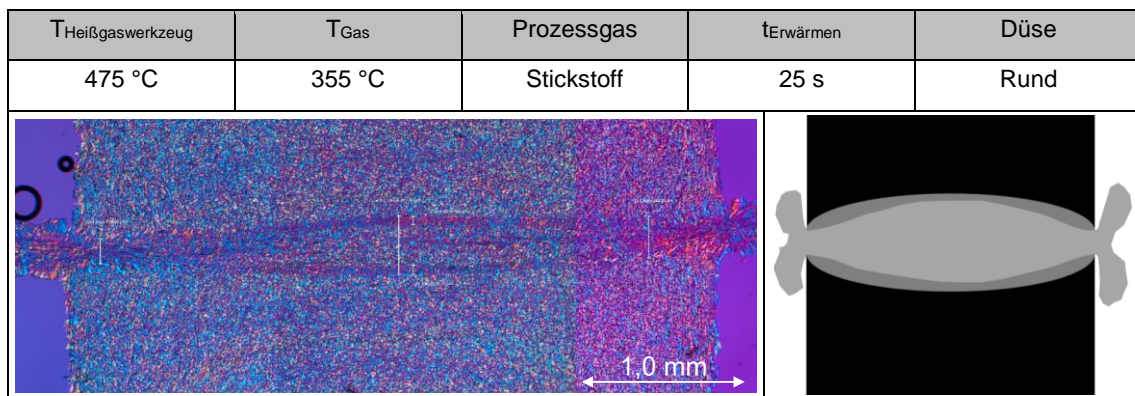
Dünnschnittaufnahme einer mit Rund-Düse erwärmten Schweißnaht mit elliptisch aufgeschmolzenem Fügebereich
